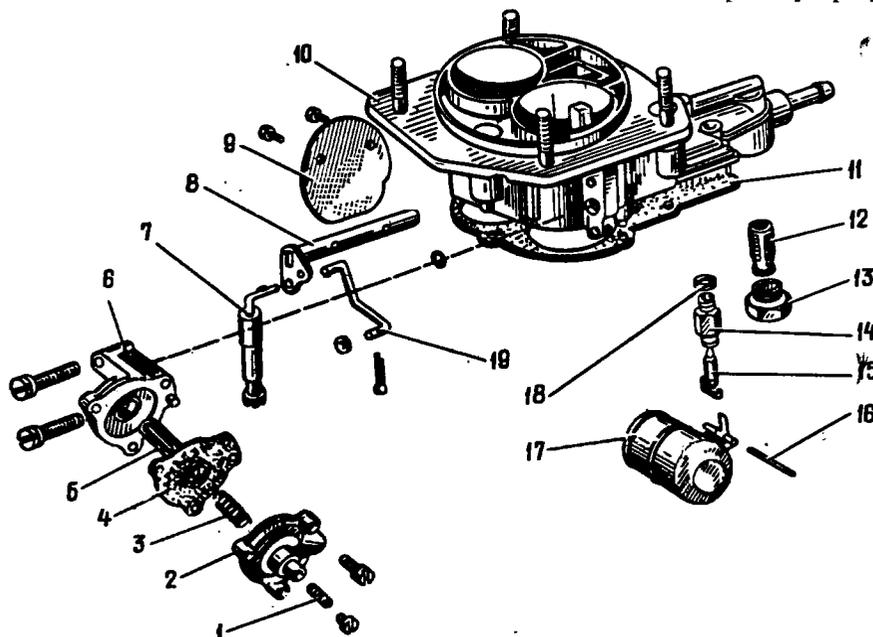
Детали крышки карбюратора 2107-1107010: 1 - регулировочный винт; 2 - крышка пускового устройства; 3 - пружина; 4 - диафрагма; 5 - шток диафрагмы; 6 - корпус пускового устройства; 7 - телескопическая тяга; 8 - ось воздушной заслонки; 9 - воздушная заслонка; 10 - крышка карбюратора; 11 - прокладка; 12 - фильтр; 13 - пробка фильтра; 14 - седло игольчатого клапана; 15 - игольчатый клапан; 16 - ось поплавка; 17 - поплавок; 18 - прокладка; 19 - тяга пускового устройства
